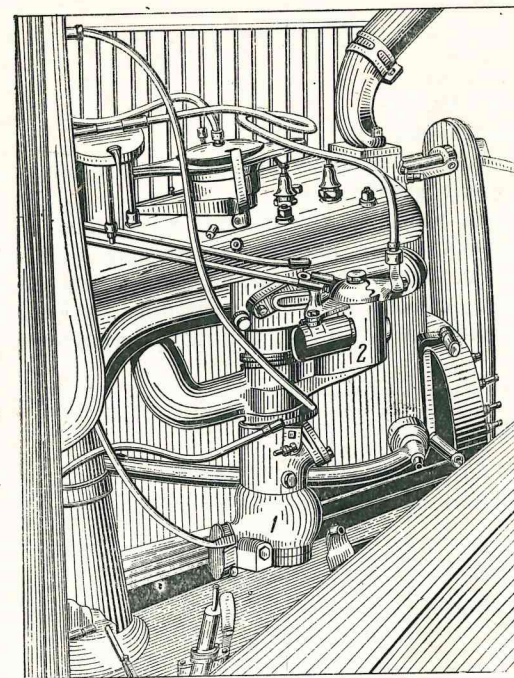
Схема подвода газа в двигатель через карбюратор.
